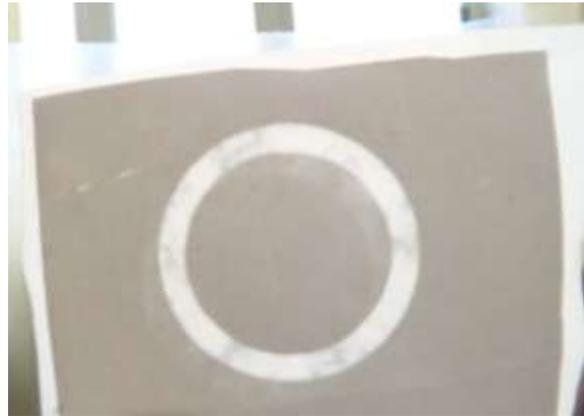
Образец фильтрующей мембраны с кольцевым сварным швом на просвет.
